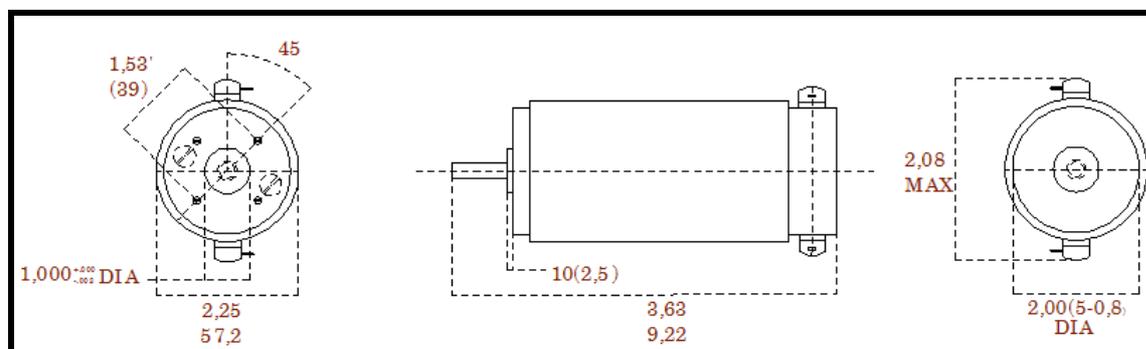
17. Dimensiones del Servomotor EG&G M2110
